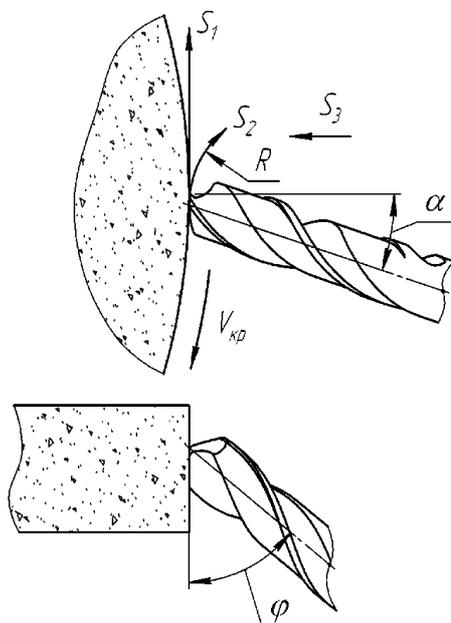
Схема заточки сверла по задней поверхности вручную
